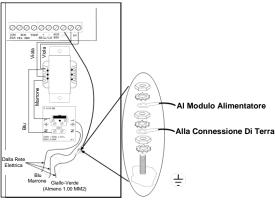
Schema di Cablaggio dell'Alimentatore
